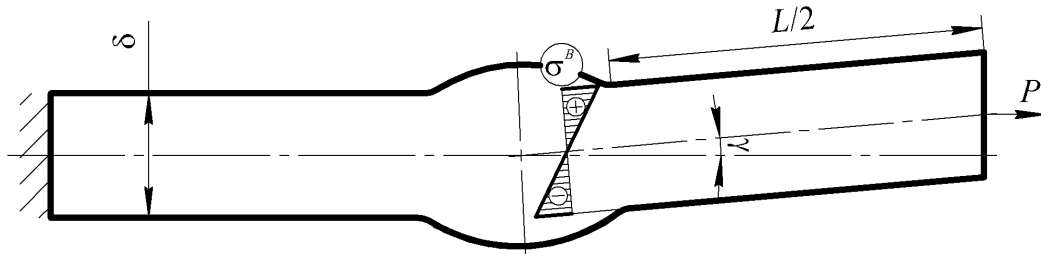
Розрахункова схема стикового зварного з'єднання з початковою кутовою деформацією.
